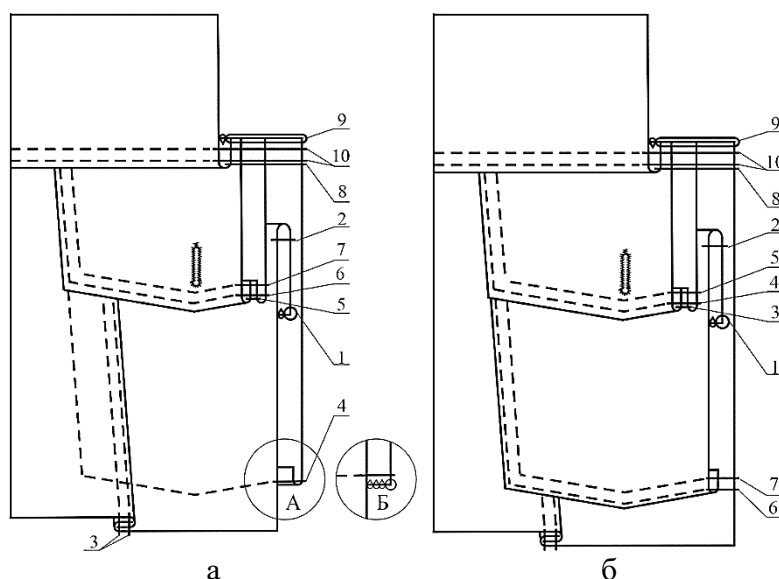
Обработка верхнего кармана с клапаном в шве соединения кокетки переда с основной деталью (рисунок авторов): а — непрорезного; б — накладного
